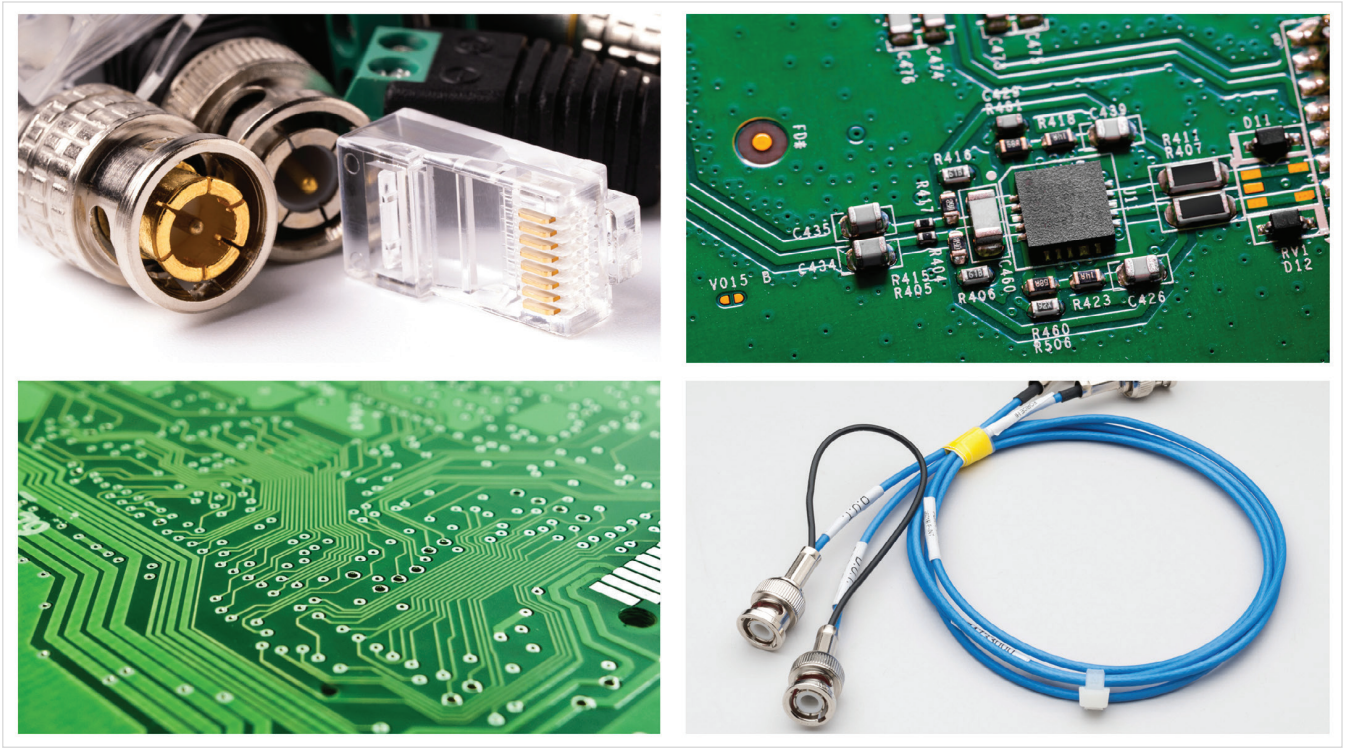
TDR 可用于测量裸装或已装配的 PCB、电缆和连接器的传输线特性。
